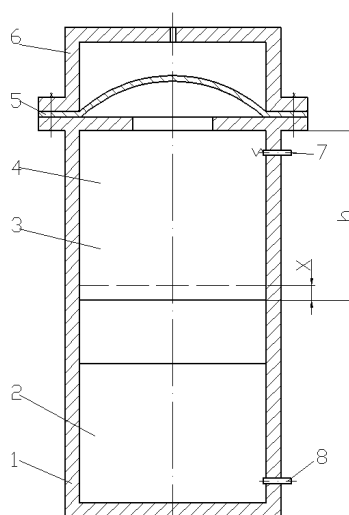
Расчетная схема рабочего процесса двухкамерного устройства для штамповки: 1 – корпус; 2, 4 – камеры сгорания; 3 – поршень; 5 – штампуемая заготовка; 6 – матрица; 7, 8 – свечи зажигания
